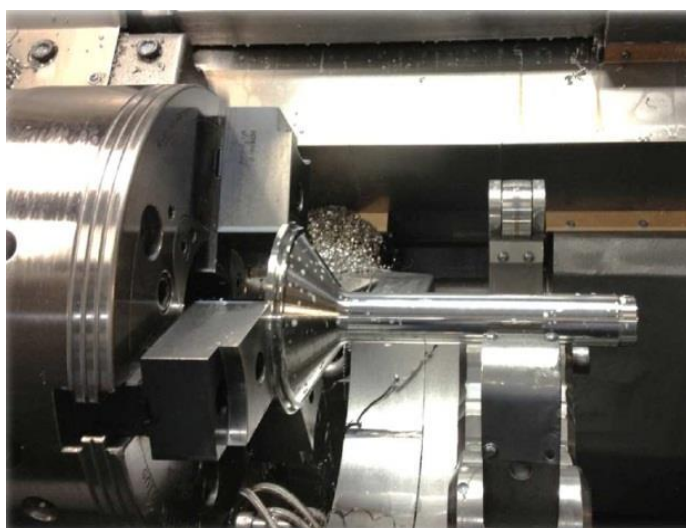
Sistema de fixação do disco de válvula na máquina de usinagem.
